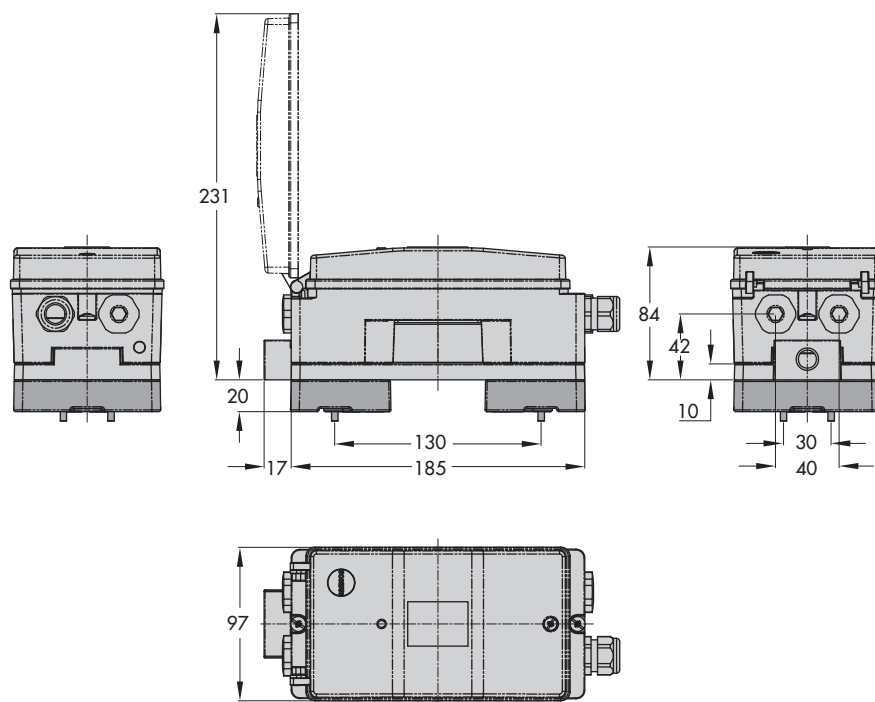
· Dimensions du boîtier de fins de course type 3738
